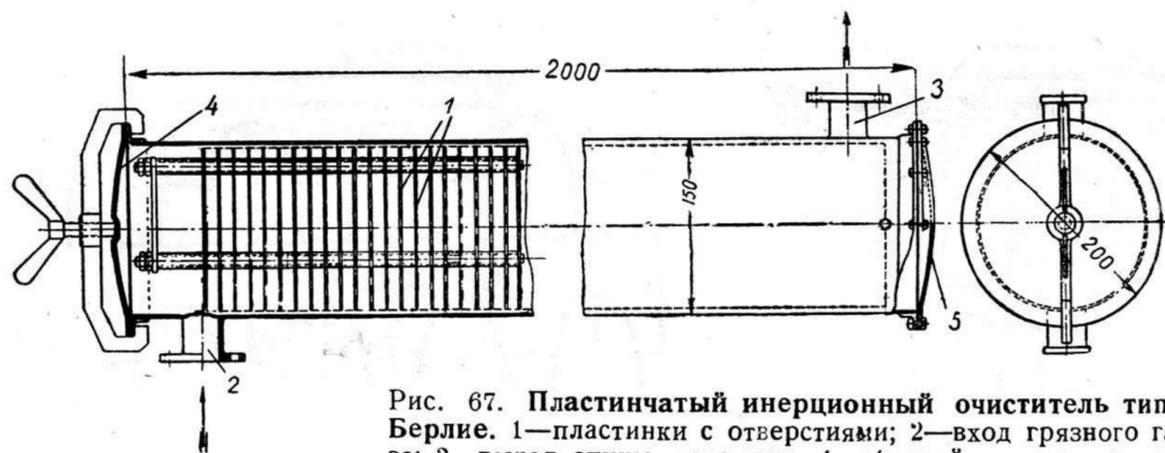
Пластинчатый инерционный очиститель типа Берлие. 1—пластинки с отверстиями; 2—вход грязного газа; 3—выход очищенного газа, 4—съемный люк для очистки; 5—постоянный люк
